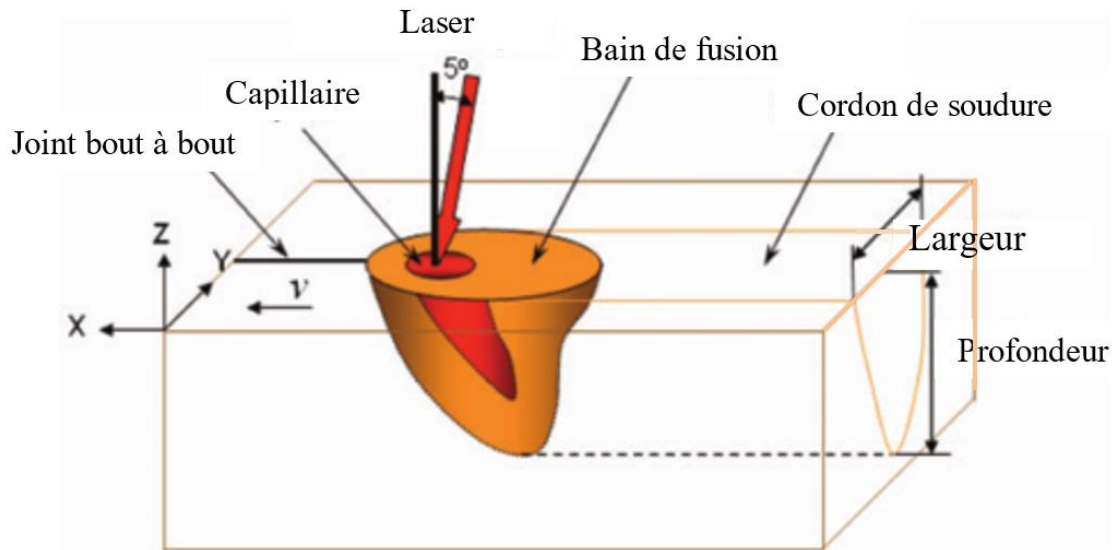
Représentation schématique du soudage laser en trou de serrure [1]
